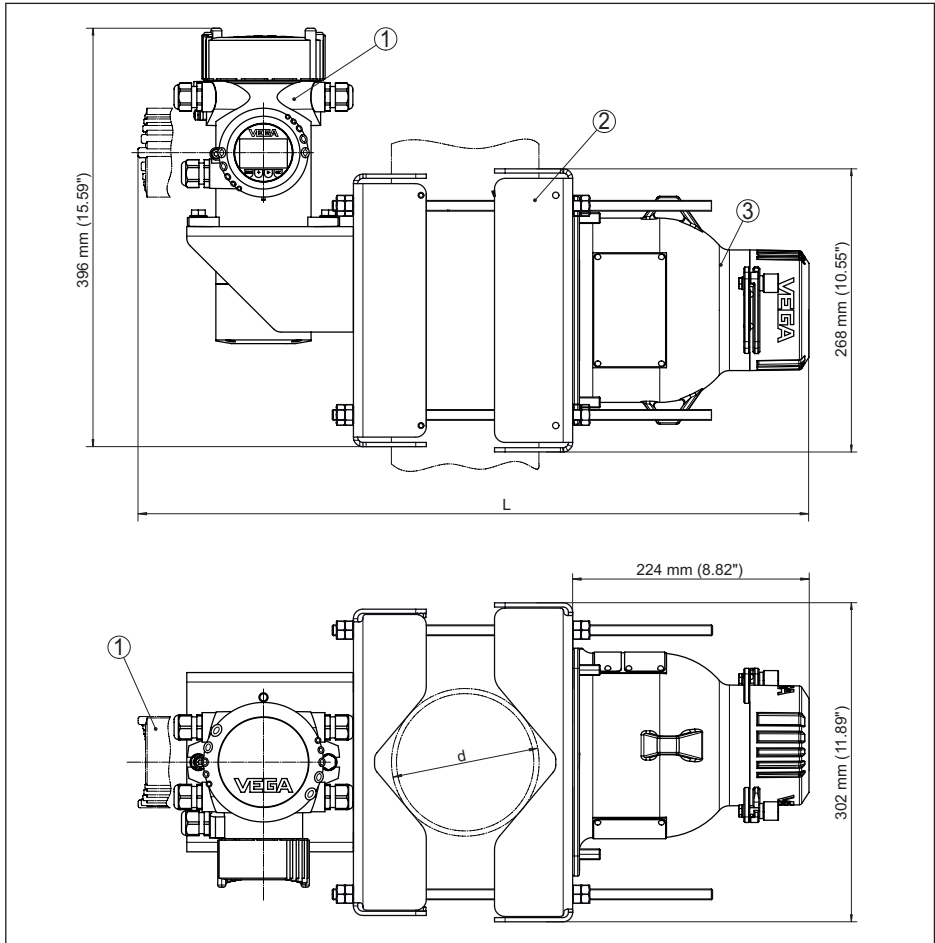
Klemmvorrichtung mit senkrecht montiertem Sensor (mit VEGASOURCE 81, 82, 83)
